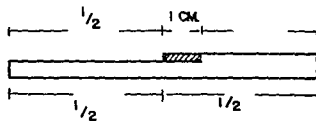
DIMENSIONES DEL CIERRE TRANSVERSAL.
